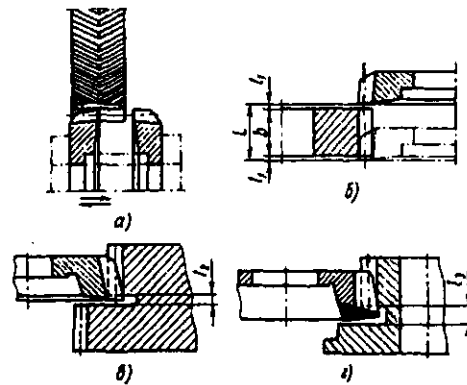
Схемы нарезания зубьев колес на зубодолбежном станке
